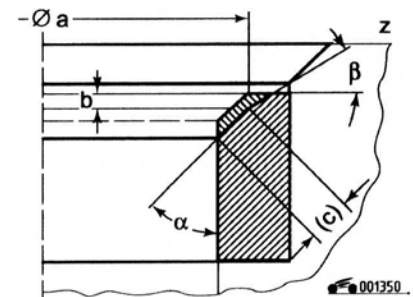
Профиль седла выпускного клапана: Z – привалочная поверхность головки блока цилиндров; a = 33,5 мм; c = 2,0–2,5 мм; a = 45°; b = 30°; g = 75°
